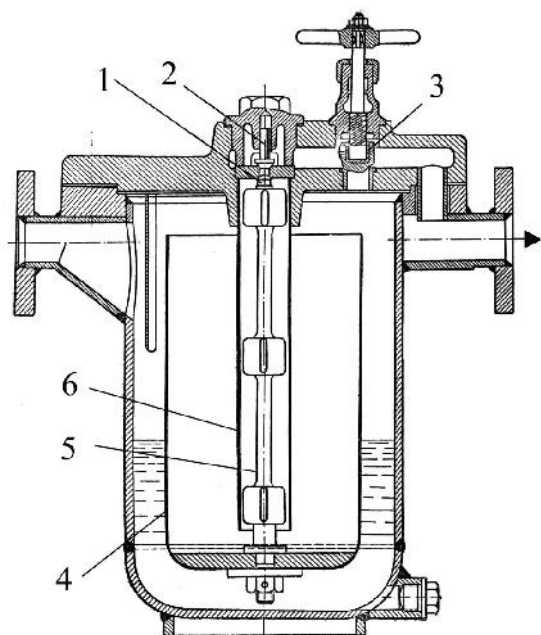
Конденсационный горшок: 1, 3 – клапан; 2 – игольчатый клапан; 4 – поплавок; 5 – шток; 6 – направляющая трубка
